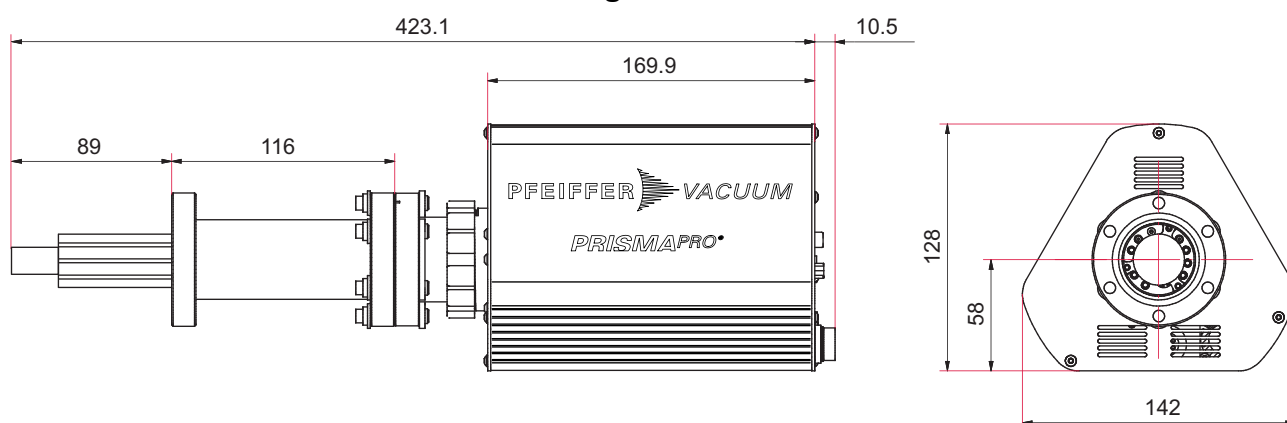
Dimensions QMG 250 M / SI à grille / QME 250 rectiligne
